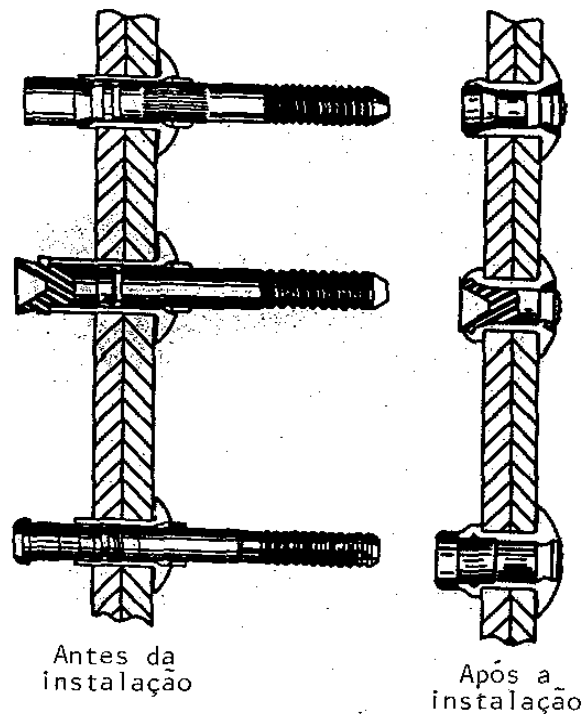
Rebites de auto-cravação (travados mecanicamente).
